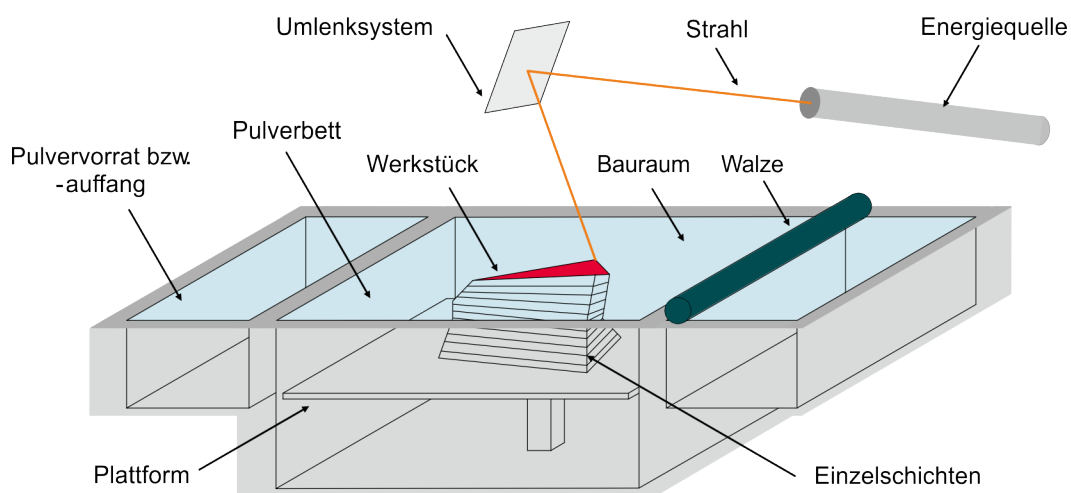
Aufbauskizze eines Pulverbettverfahrens
